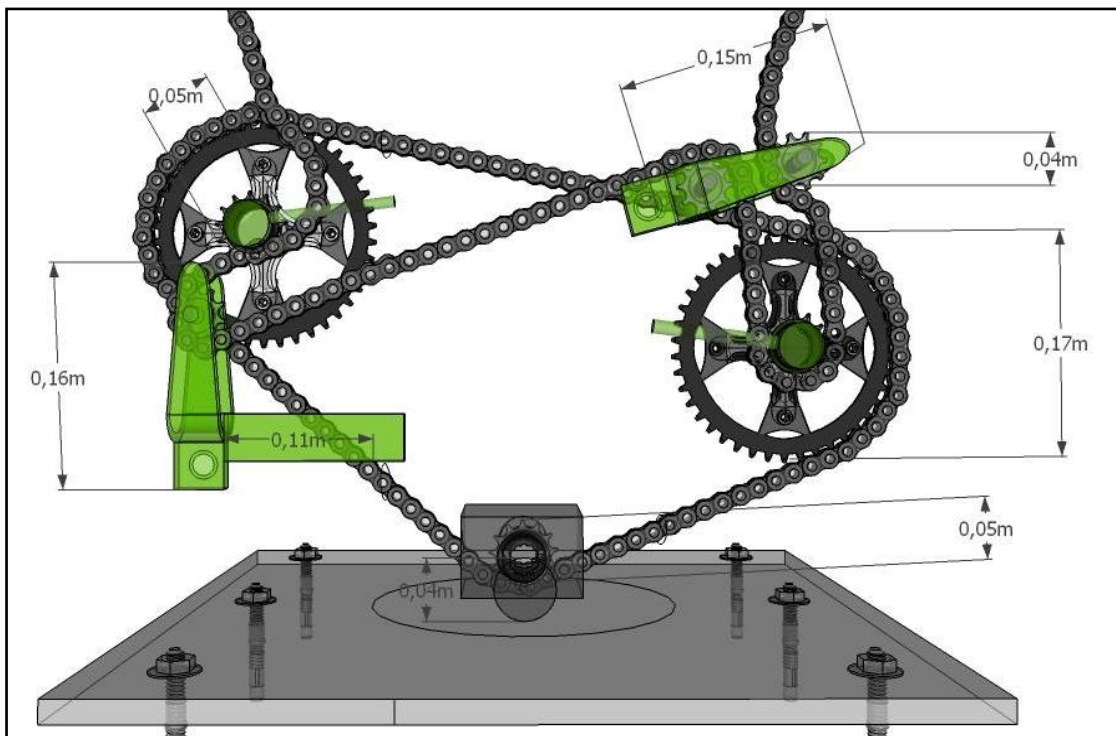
Detalle de la geometría del sistema de engranajes del subibaja a utilizar como módulo de tracción.
